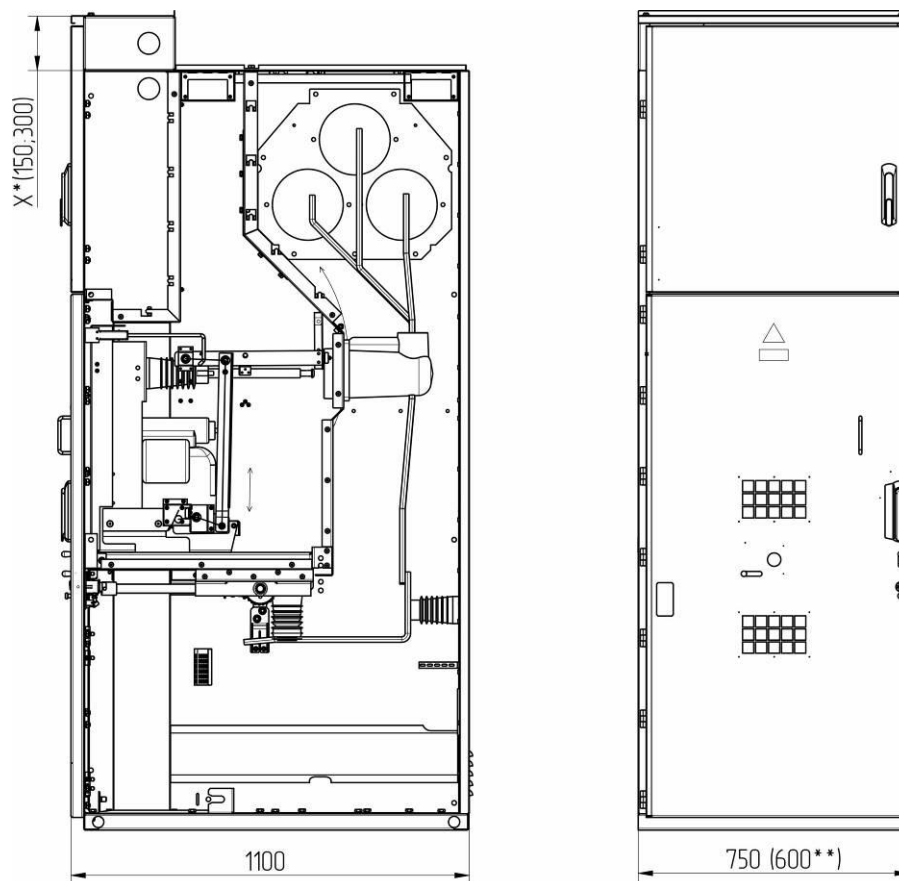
Шкаф КРУ D-12РТ с измерительными ТН и заземлителем сборных шин
